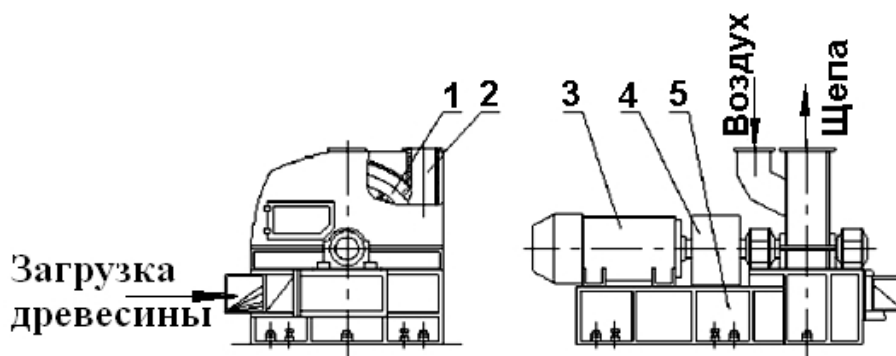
Общий вид дисковой рубительной машины с межопорным расположением диска: 1 – ротор; 2 – кожух; 3 – приводной электродвигатель; 4 – муфта с тормозом; 5 – рама с загрузочным патроном
